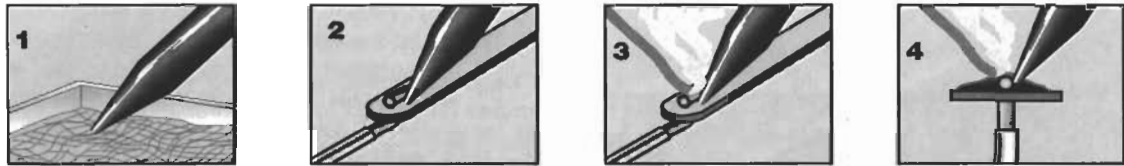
Cómo soldar alambres a terminales. Caliente la punta del cautín, límpiela con una esponja húmeda (1) y estáñela (apliquele soldadura) con el fin de evitar su oxidación. Para soldar, caliente con la punta del cautín el terminal y el alambre (2), aplique la soldadura (3) y permita que fluya uniformemente sobre la unión (4). Retire la soldadura y el cautín.
